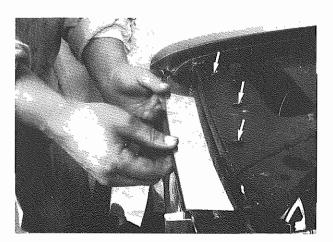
Viti di fissaggio profilo superiore Upper rim screws
